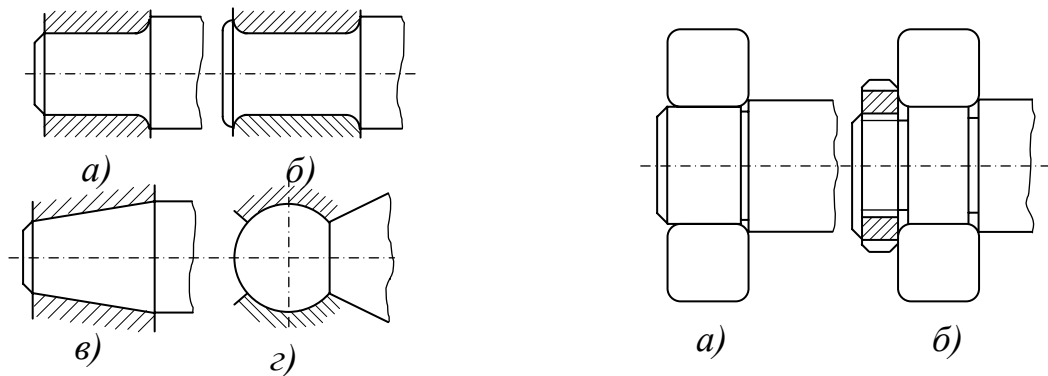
Основні типи цапф валів під підшипники ковзання
